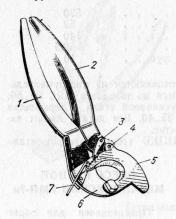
1 — ручка подвижная; 2 — трос; 3 — рычаг; 4 — корпус; 5 — матрица; 6 — сектор зубчатый; 7 — рейка с пуансоном; 8 — барабан
